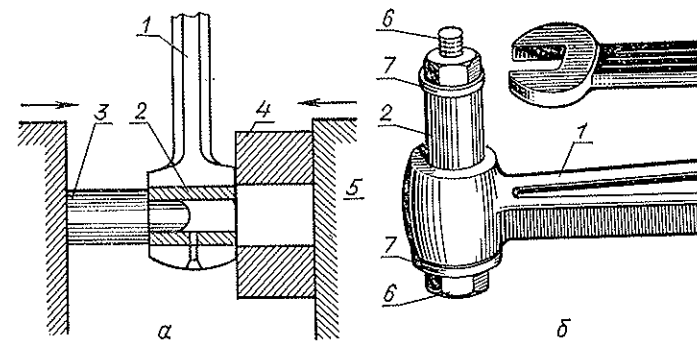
Приспособление для запрессовки и выпрессовки втулки верхней головки шатуна:
